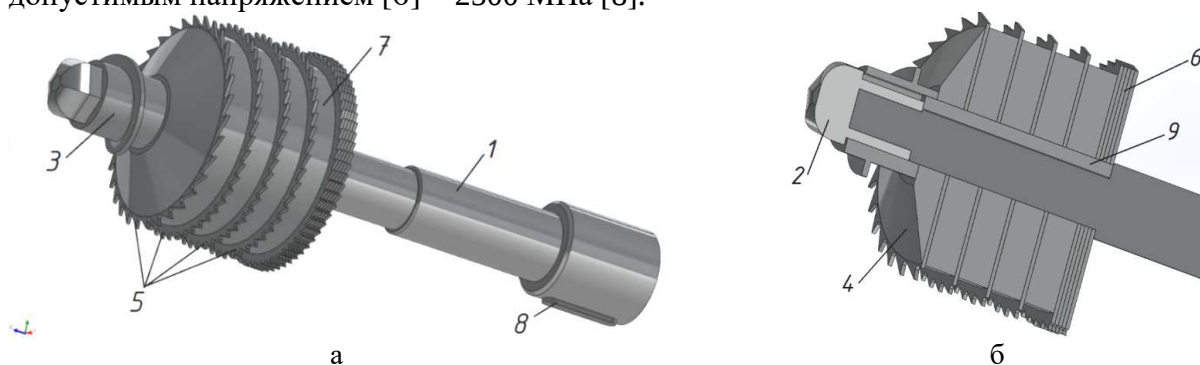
Цифровая модель вертикального ротора в сборе: а – общий вид ротора; б – разрез режущую часть ротора
